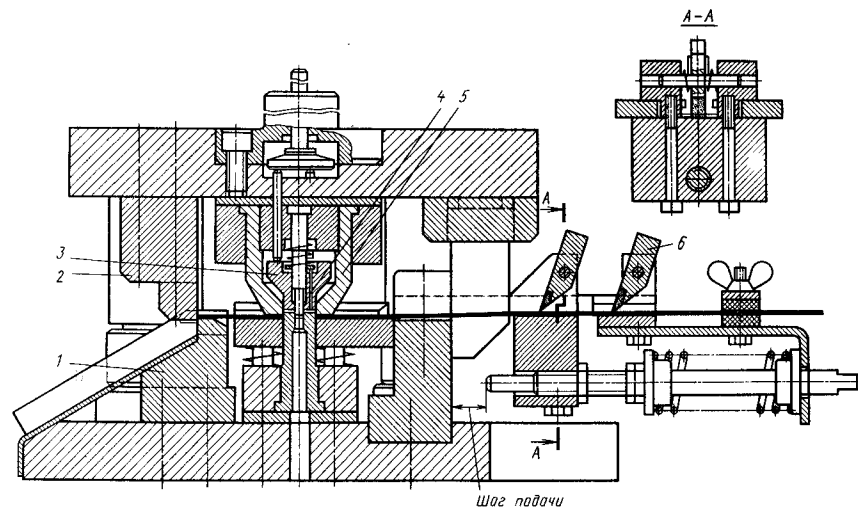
Механизированный штамп совмещенного действия с отлипателем вырубленных деталей от выталкивателя
